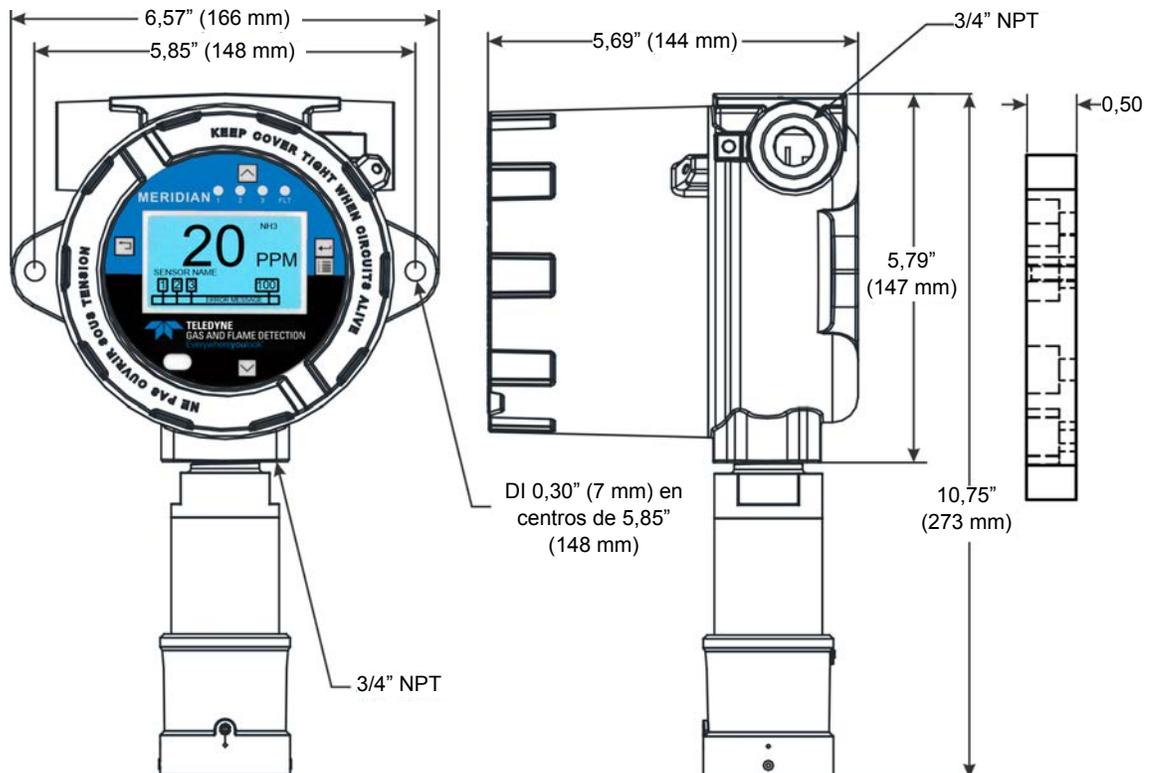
Dimensiones de montaje del dispositivo - Aluminio y acero inoxidable
